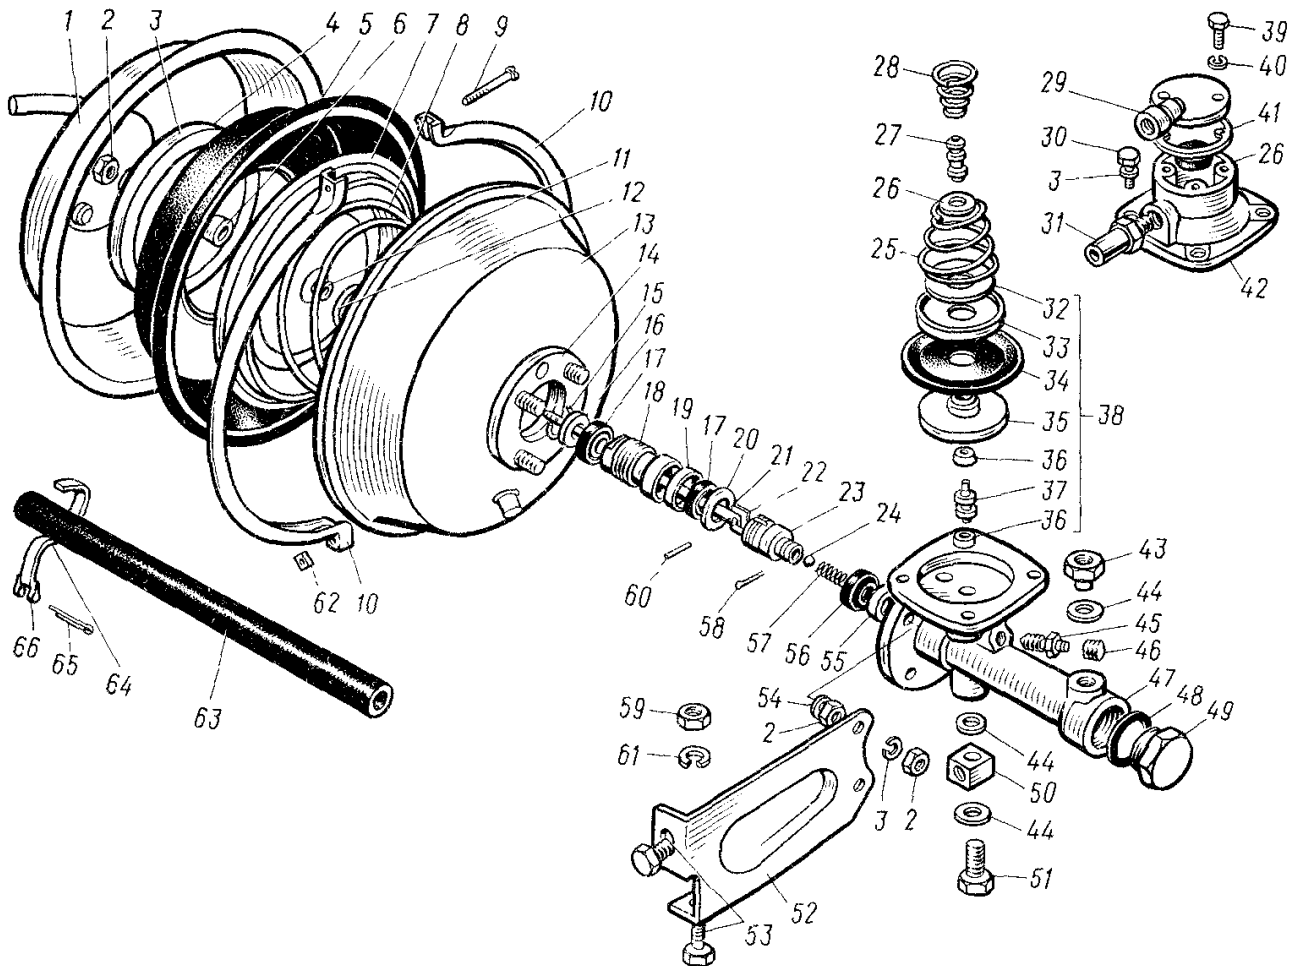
Гидровакуумный усилитель в разобранном виде:
